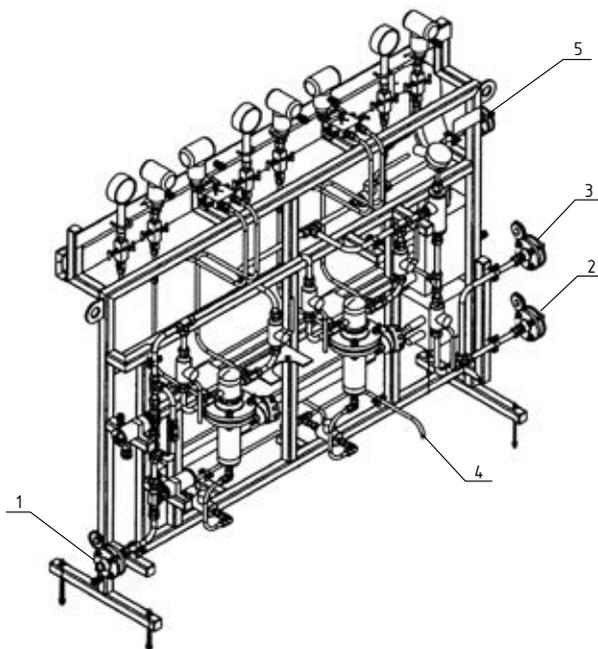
Общий вид блока подготовки инструментального и барьерного азота: 1 – вход азота; 2 – выход барьерного азота; 3 – выход инструментального азота; 4 – дренаж фильтров; 5 – сборс на свечу
